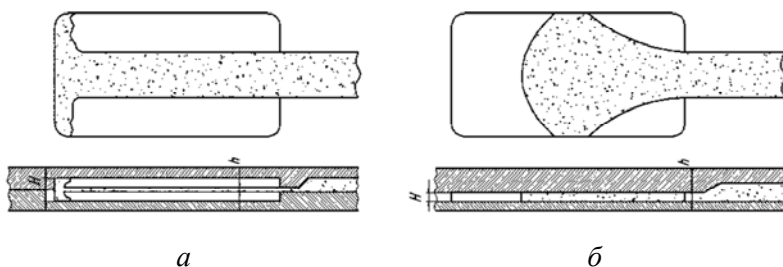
Направление потока металла при различных соотношениях толщины отливки и питателя
